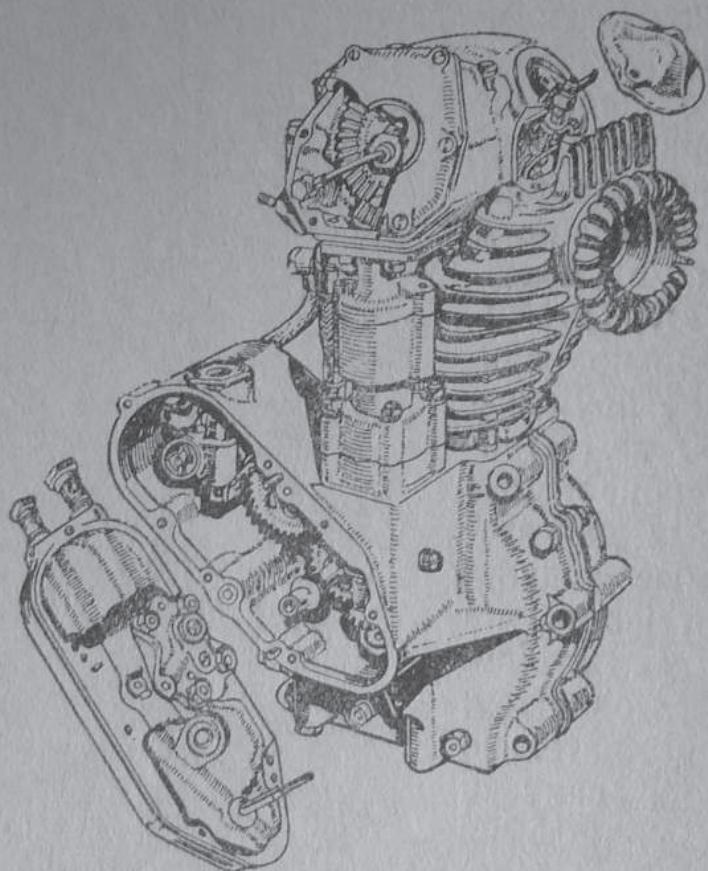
Схема устройства клапанного механизма верхнеклапанного двигателя.
